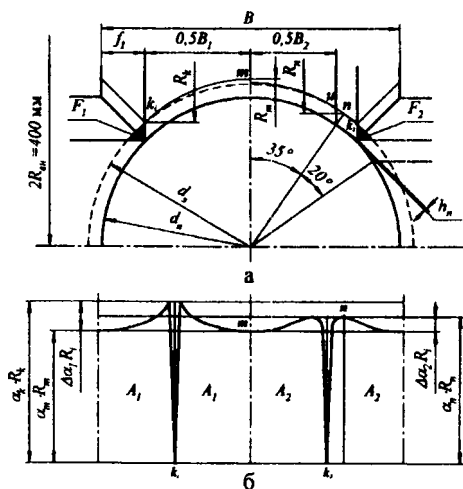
Схема калибровок «круг-круг» (а) и поверхности контакта валков с заготовкой (б) в четырехвалковом калибре
